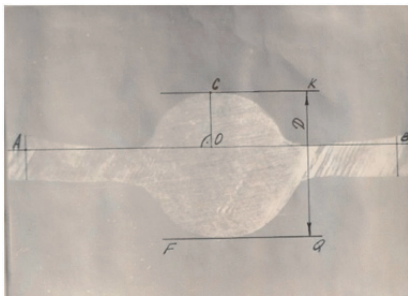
Поперечное сечение контрольной поковки после изготовления 2000 деталей, образец №10'
